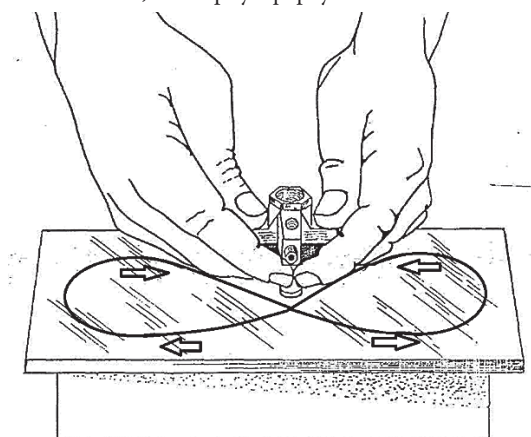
Ручная притирка уплотнительного торца корпуса форсунки.
